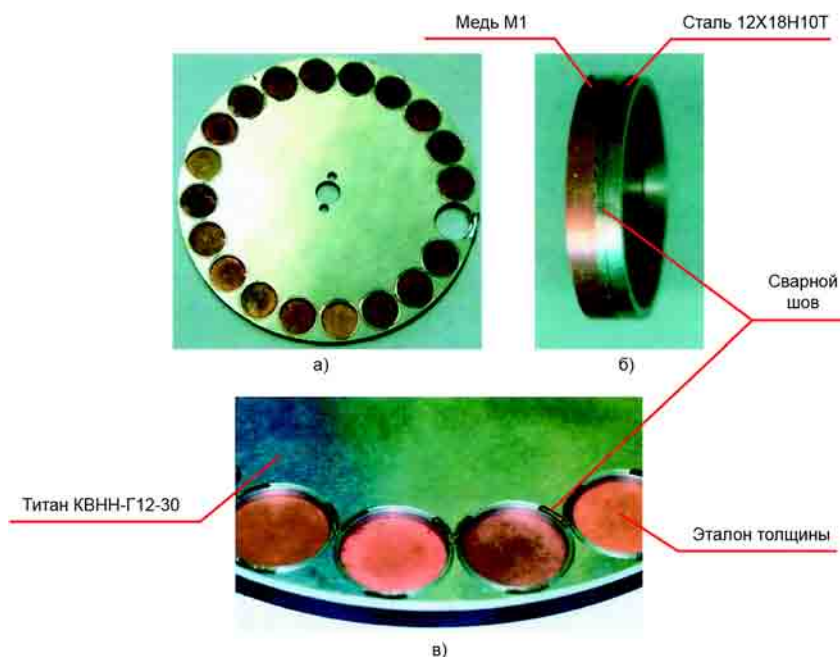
Узел калибратора-дискдержателя эталонных образцов, сваренный импульсной лазерной сваркой: а — держатель эталонных образцов — титановый диск; б — эталонный образец толщин меди; в — титановый диск
